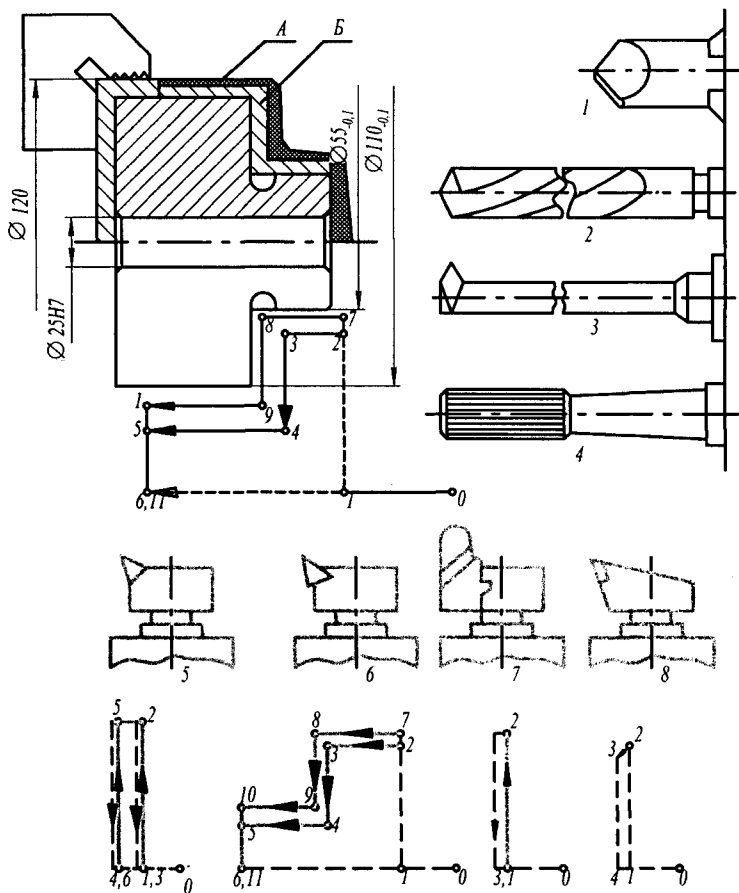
Схема обробки зубчастого колеса на токарно-револьверному верстаті з ЧПУ.
